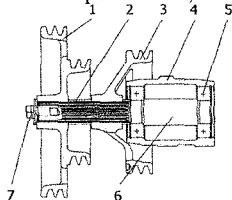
Контрпривод ИРС: 1, 3 – шкив; 2 – втулка; 4 – корпус подшипников; 5 – подшипник; 6 – вал; 7 – болт
